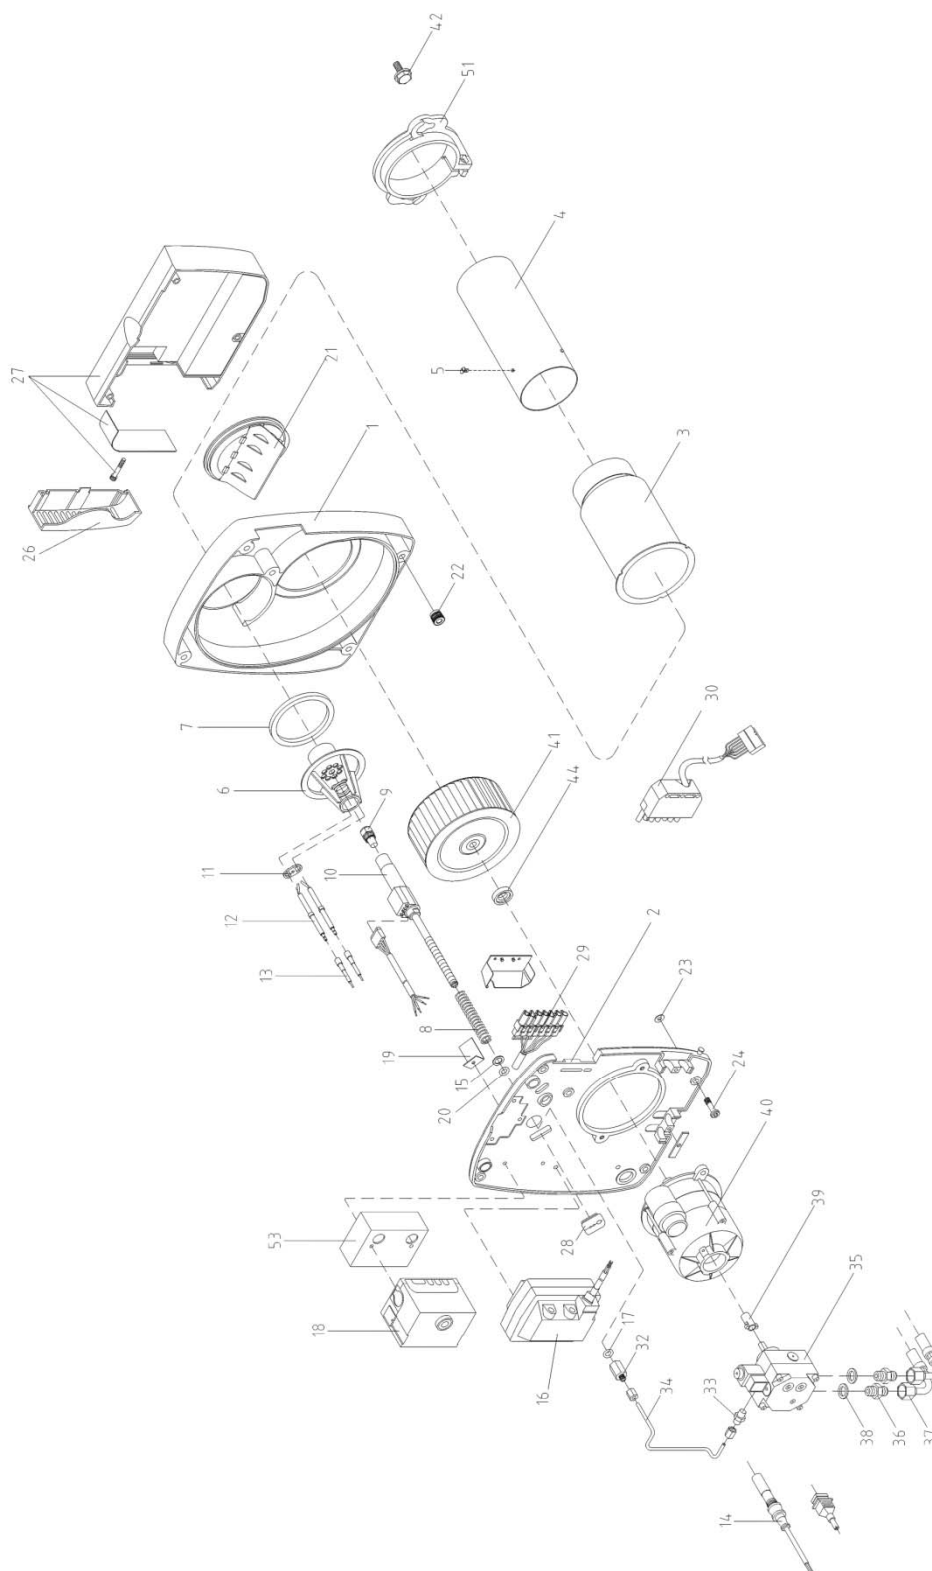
Explosionszeichnung ECOHEAT ÖI SC ... für BNR 1 HUN
